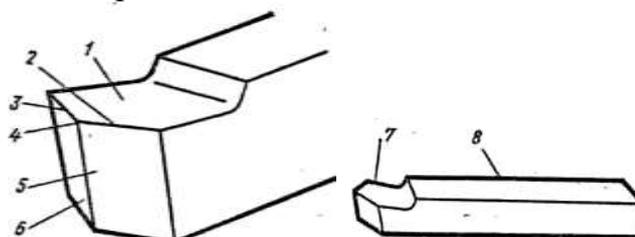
Элементы резца: 1—передняя поверхность, 2—главная режущая кромка, 3— вспомогательная задняя поверхность, 4—вершина резца, 5—главная задняя поверхность, 6— вспомогательная режущая кромка, 7— режущая часть, 8— стержень.
